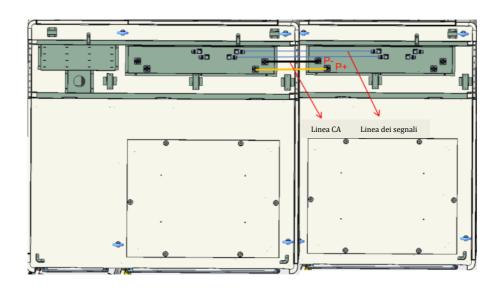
Cablaggio del cavo tra armadio di accumulo dell'energia e armadio della batteria
